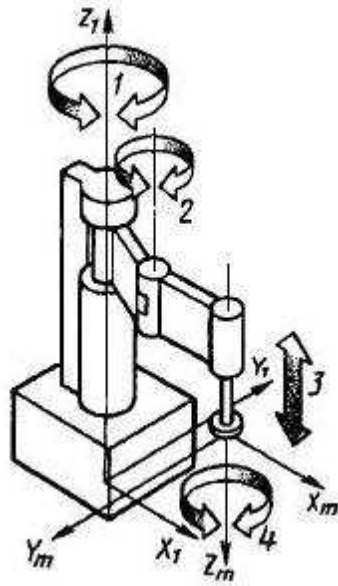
Робот, действующий в ангулярной цилиндрической, или сложной цилиндрической, системе координат.
